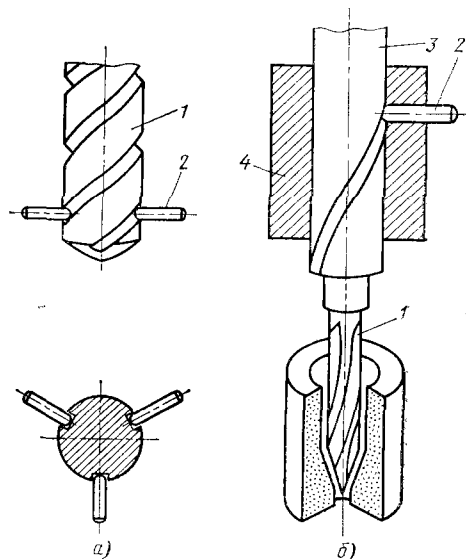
Образование винтовых отверстий электрод-инструментом, направляемым штифтами
